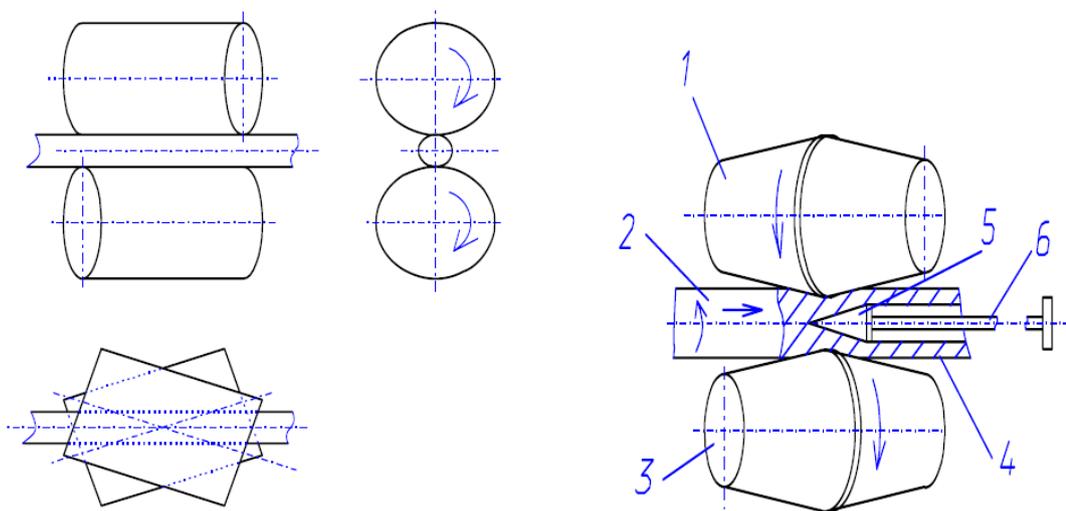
Основні схеми поперечно- гвинтової прокатки:
